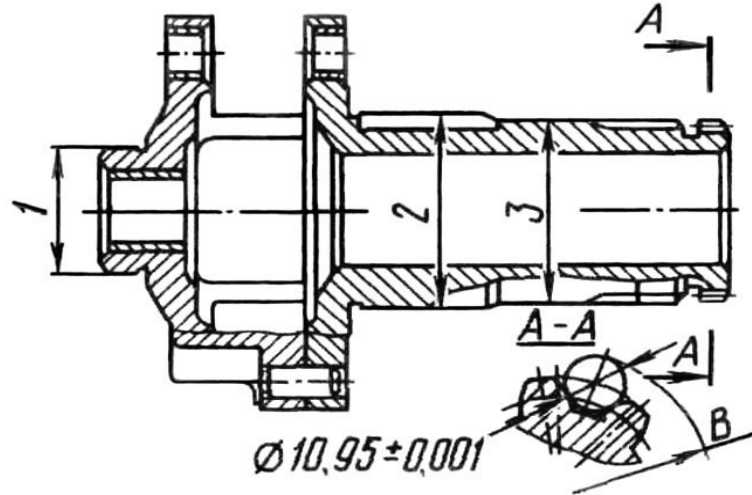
Расположение шеек водила несимметричного дифференциала в сборе с чашкой и втулками:
